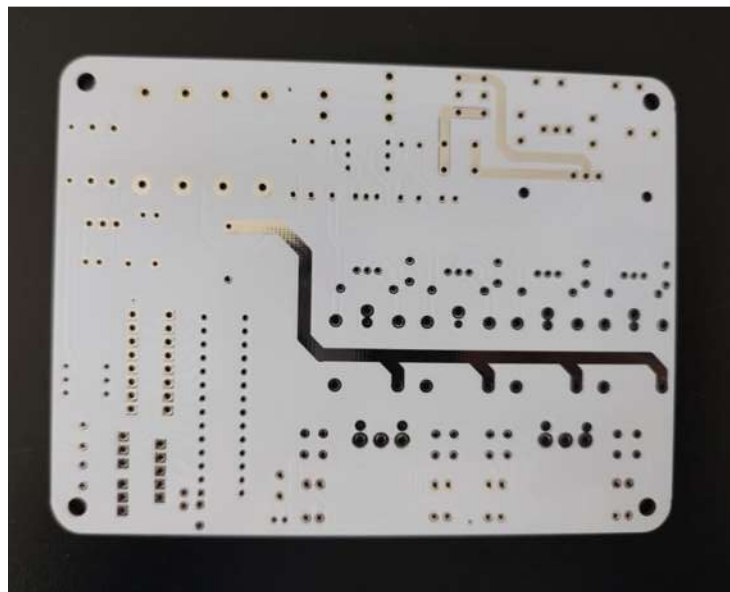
DISEÑO DEL PCB PARTE TRASERA
